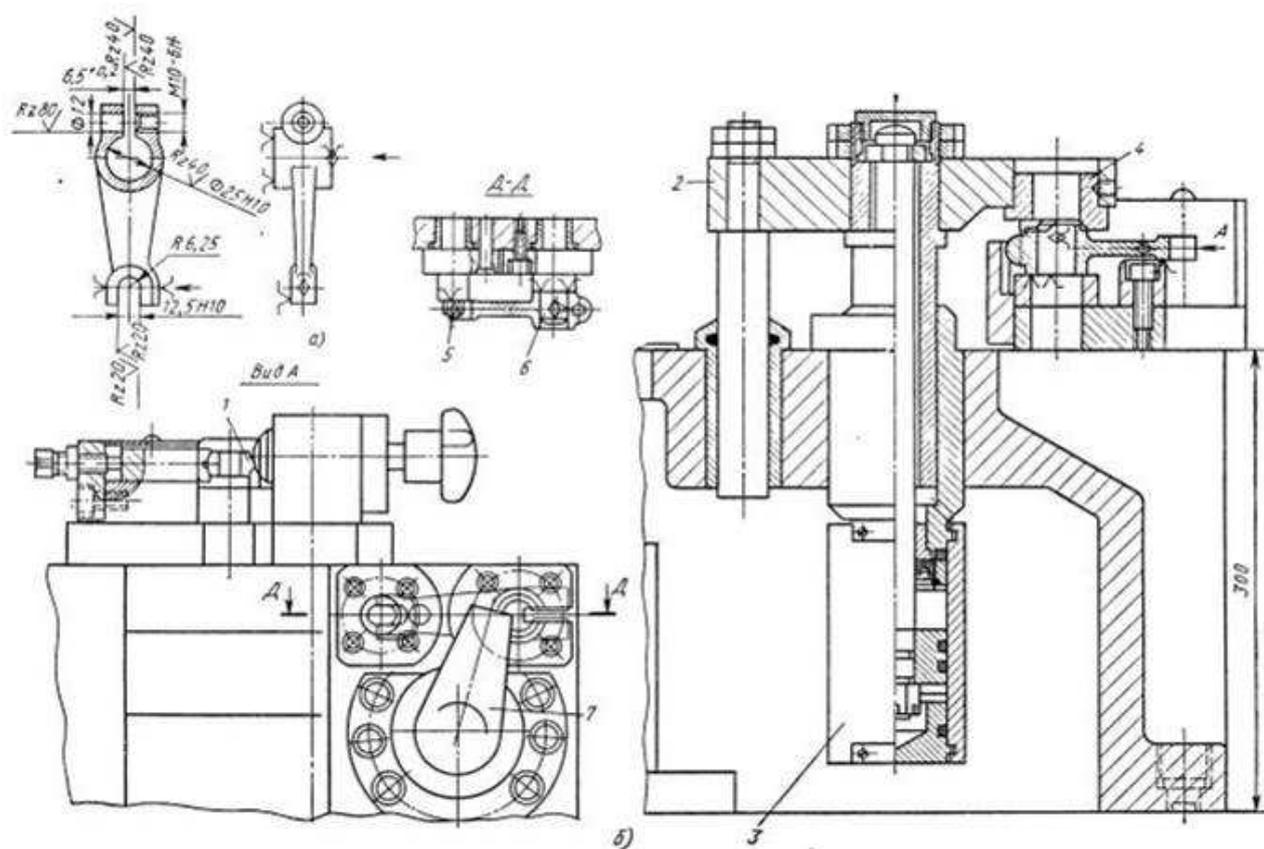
Приспособление (б) для изготовления деталей, подобных вилке включения (а)
